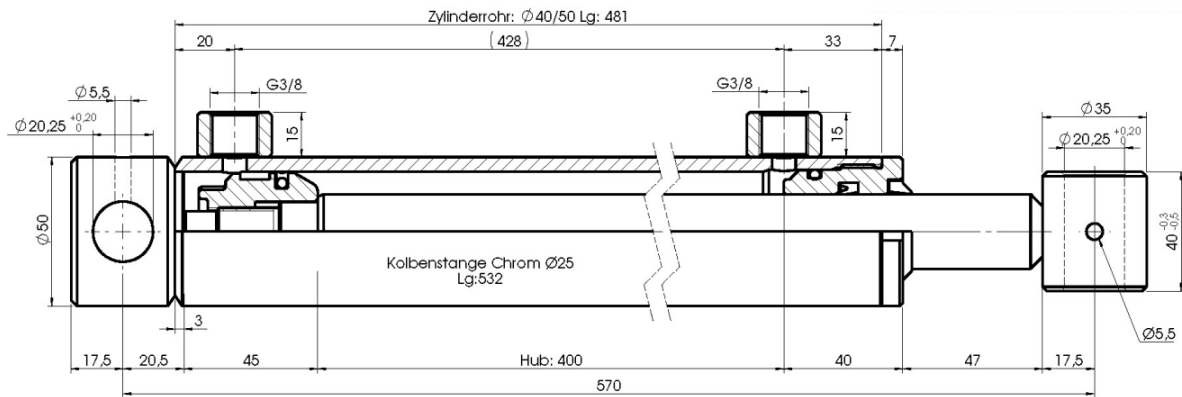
Technische Zeichnung des verwendeten Hydraulikkolbens
